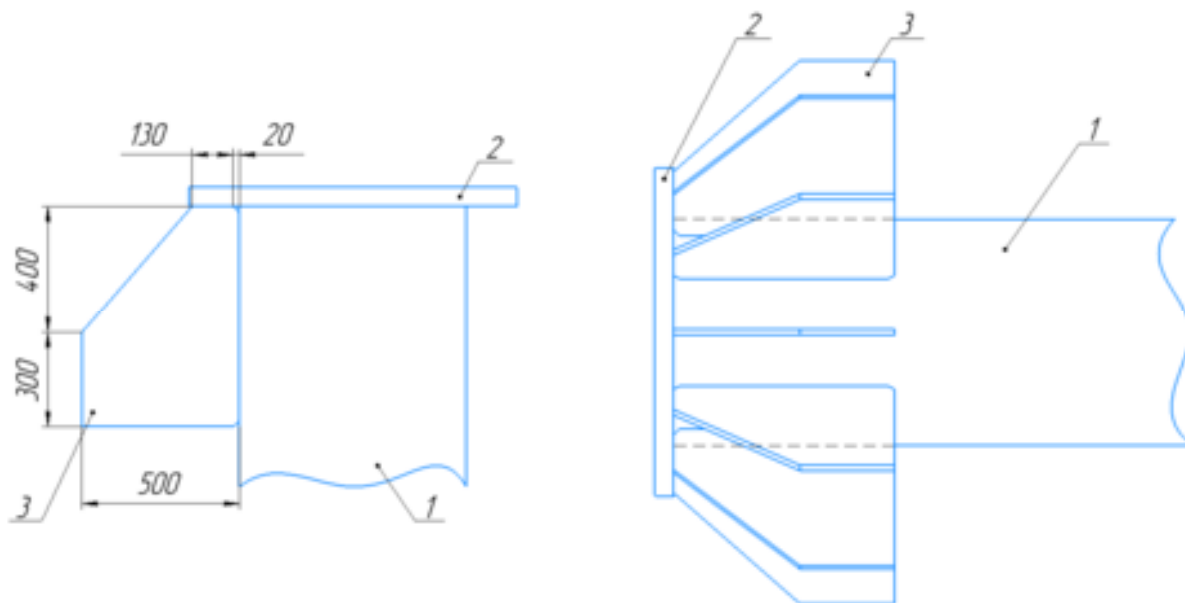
Сварка 12 листов 3 с листом профилем 1040x60 и трубой 1
